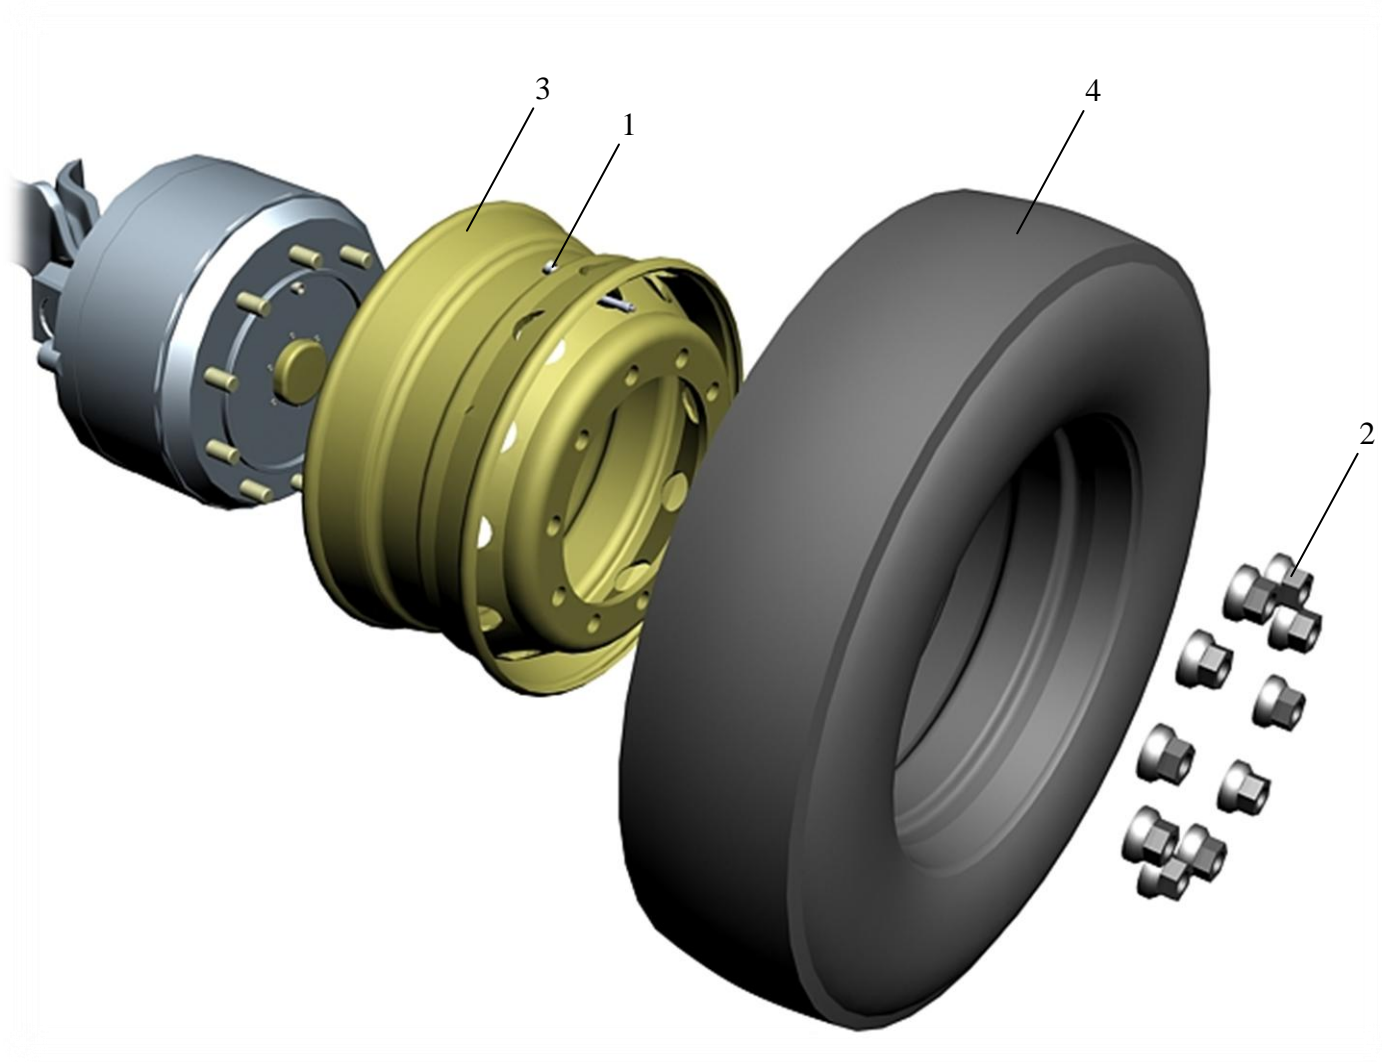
Установка одинарного колеса АКСМ 32102-210200.000
